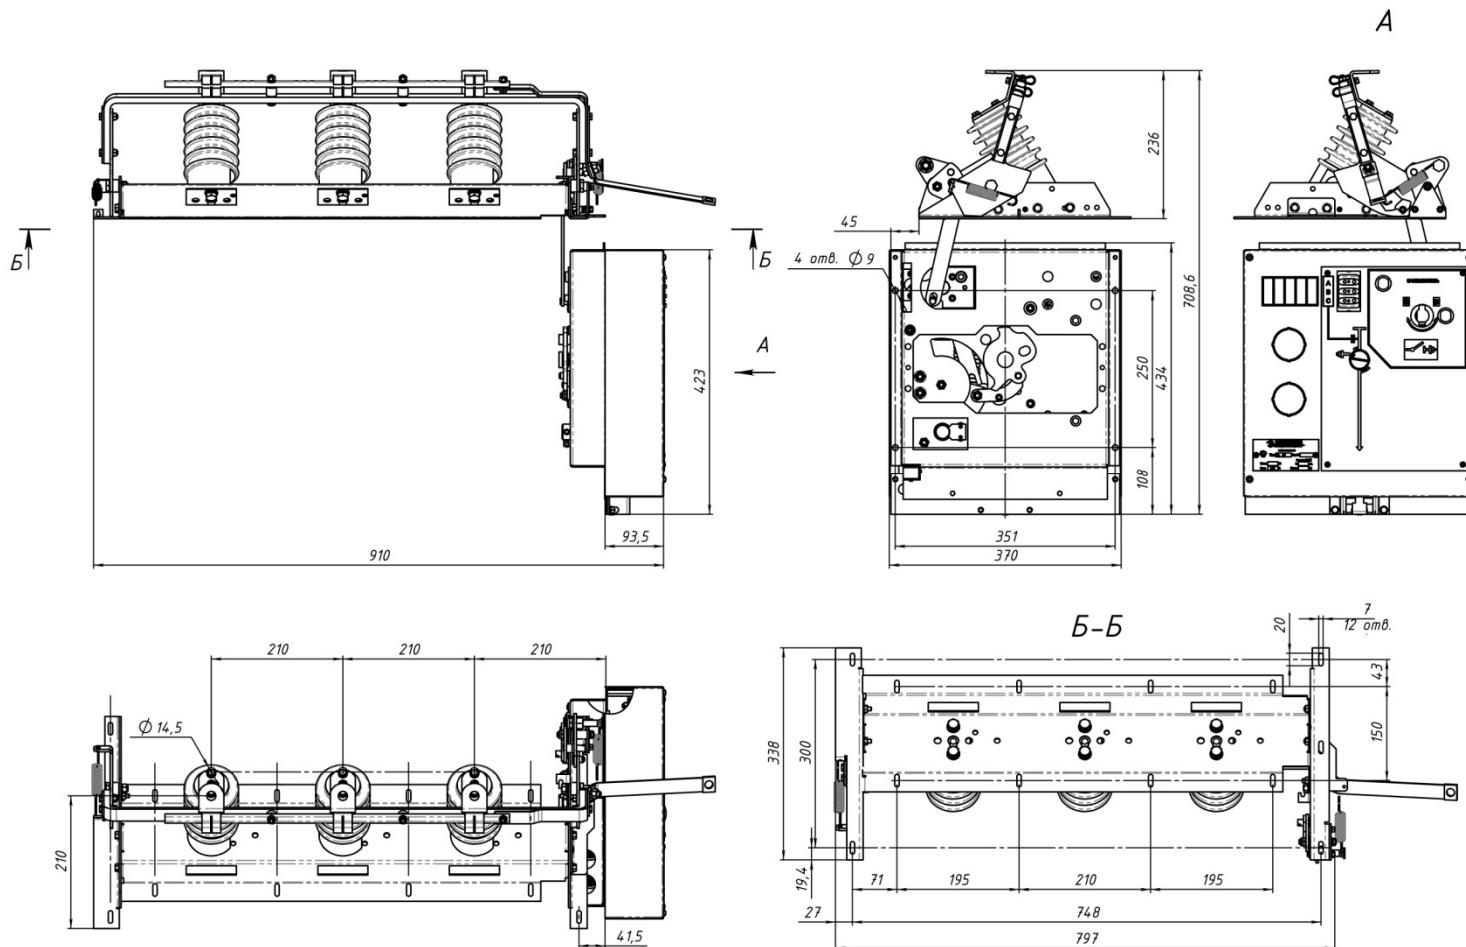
Габаритно-присоединительные размеры аппаратов типов SL12-EH(C, D)
